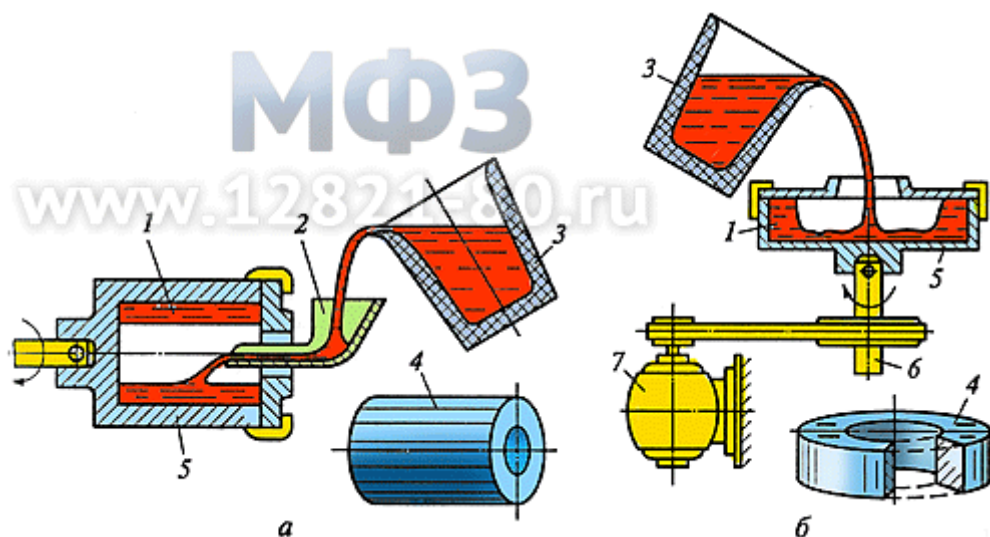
Схема изготовления отливок центробежным литьем при вращении формы:
